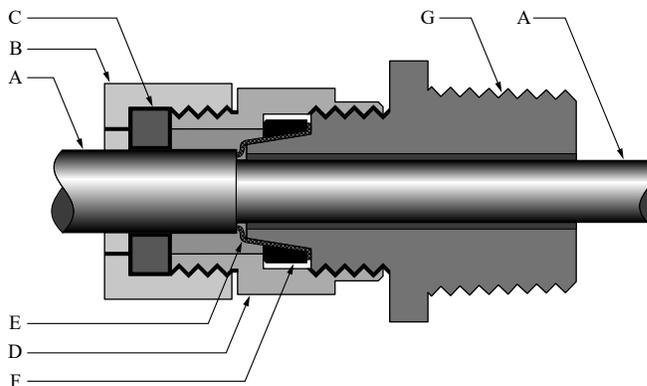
Kabelverschraubung und Kabel (Explosionsdarstellung)
